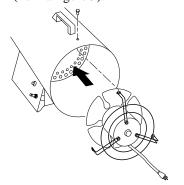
Remise en place du moteur et de la grille du ventilateur
